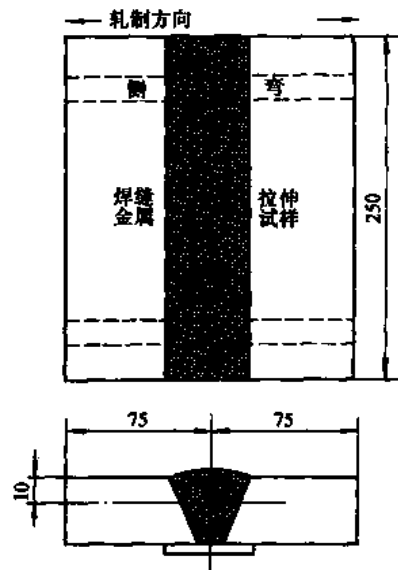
角焊缝焊接材料评定试板形式和尺寸及取样部位
